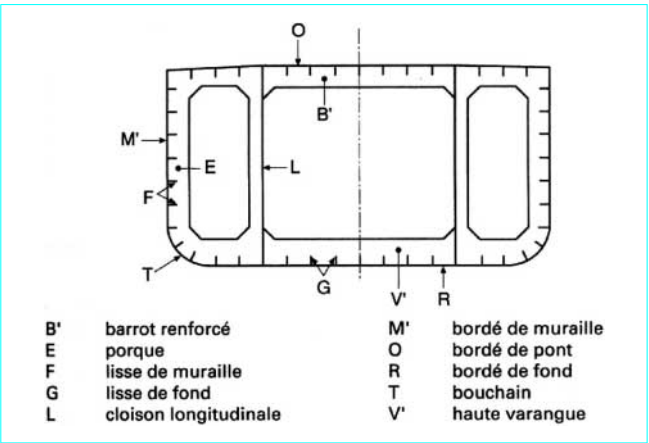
Structure de la coque d'un navire : construction longitudinale
